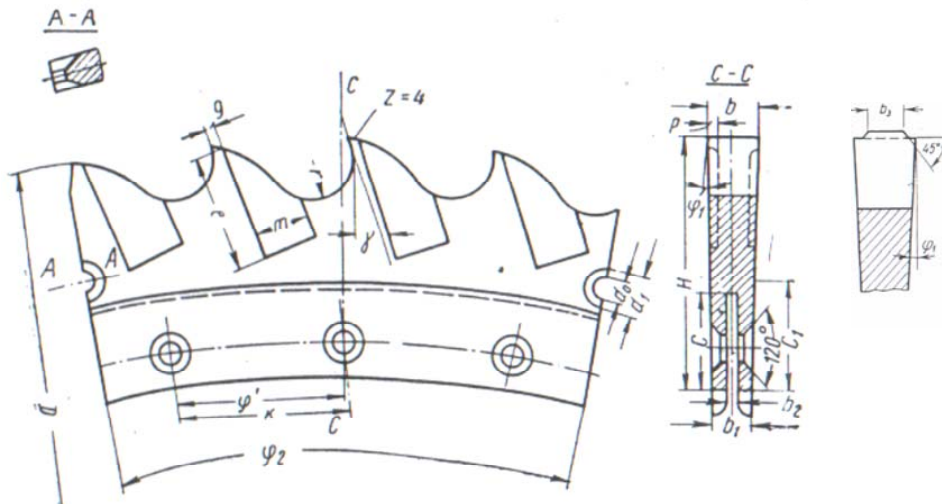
Зубчатые сегменты из быстрорежущих сталей для установки на дисковых пилах
